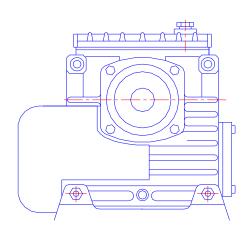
червячный редуктор 2Ч-40-50-51-3-УЗ ТУУ 29.1 24587
